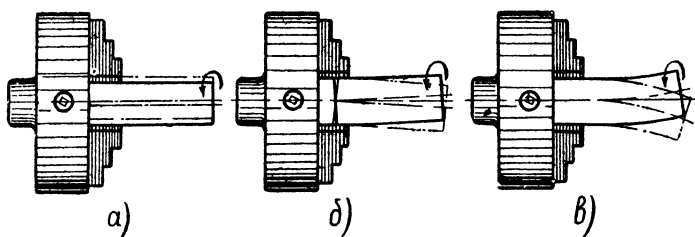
Различные положения заготовки при зажиме ее в патроне:
